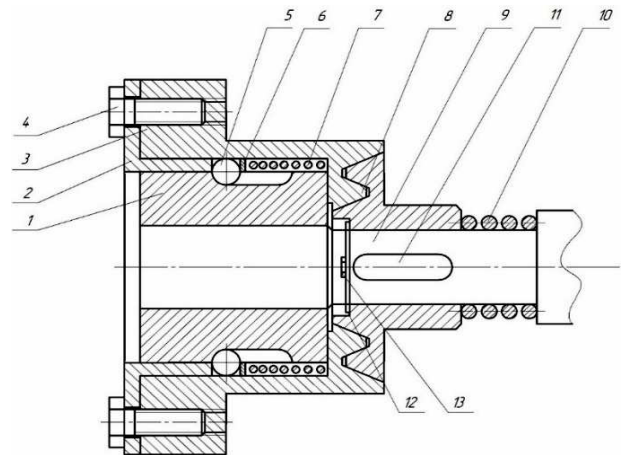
Загальний вигляд кулькової обгінно-запобіжної муфти із конічними фрикційними поверхнями запобіжної частини в робочому стані
